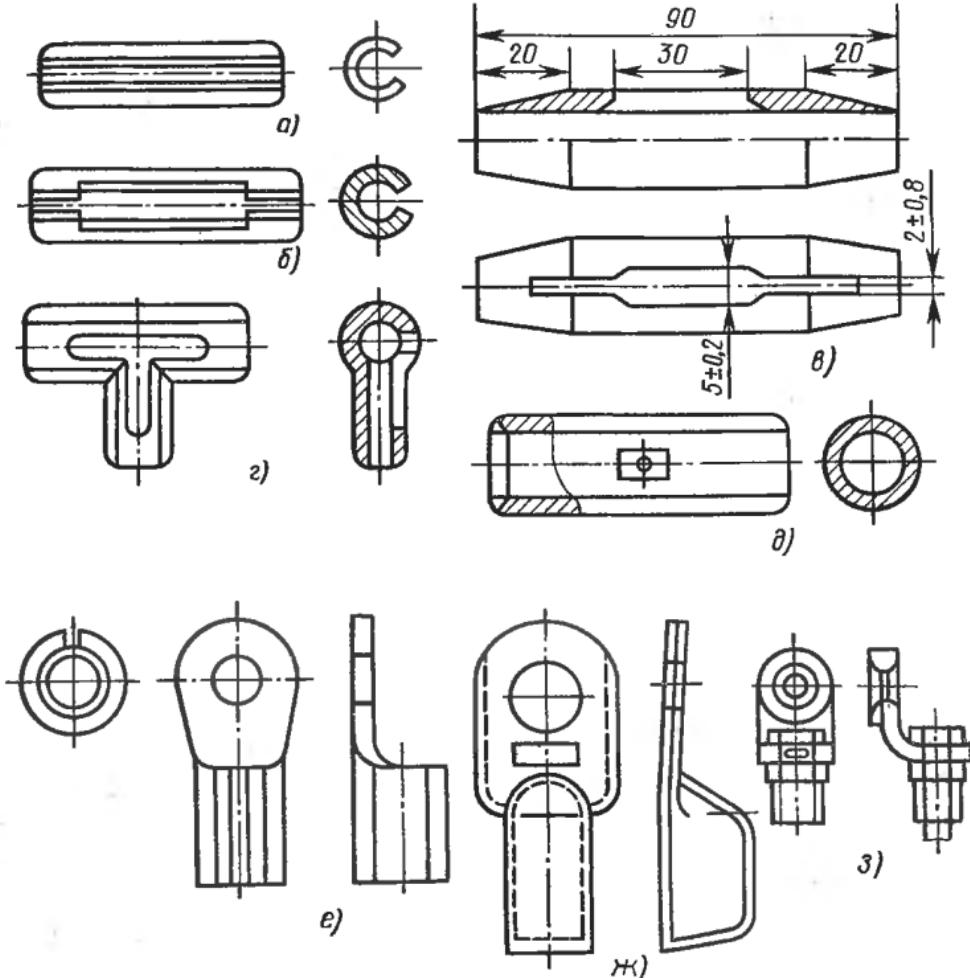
Гильзы и наконечники для пайки, опрессовки и сварки жил проводов и кабелей:
